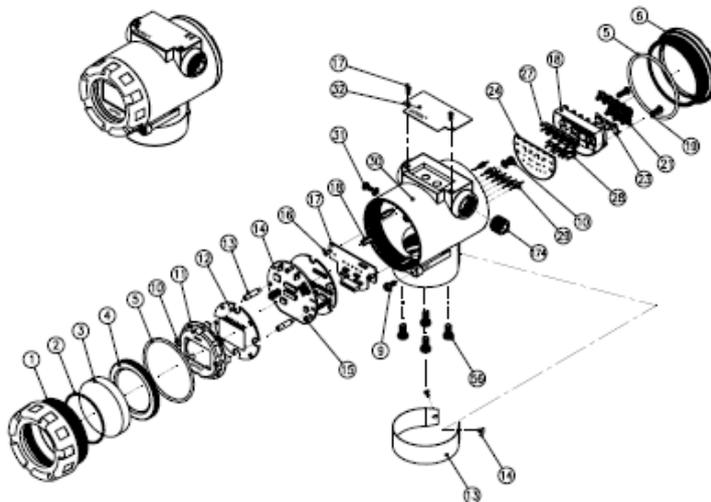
Model ATT-2100 Transmitter Expoded View (Housing)
